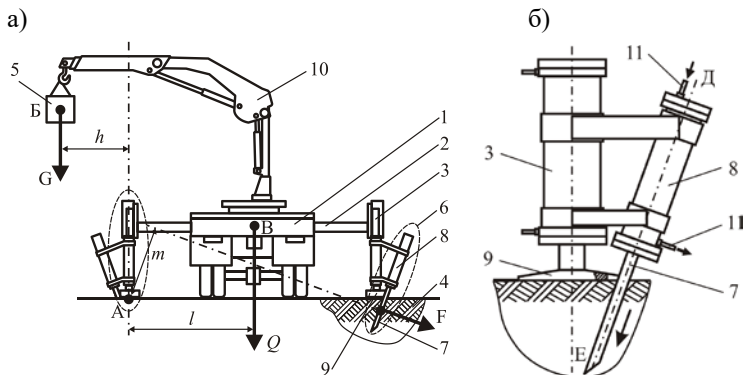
Выносная опора с возможностью анкеровки [12]: а – установка на шасси базовой машины; б – общий вид (1 – рама мобильной транспортно-технологической машины; 2 – кронштейн; 3 – опорное устройство с гидроприводом; 4 – грунт; 5 – транспортируемый груз; 6 – анкерное устройство; 7 – рабочий элемент анкерного устройства; 8 – гидропривод рабочего элемента анкерного устройства; 9 – опорная плита; 10 – манипуляционная система; 5 – штуцеры для подвода рабочей жидкости)
